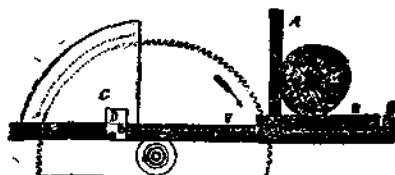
Предохранительное приспособление для поперечной круглой пилы.
